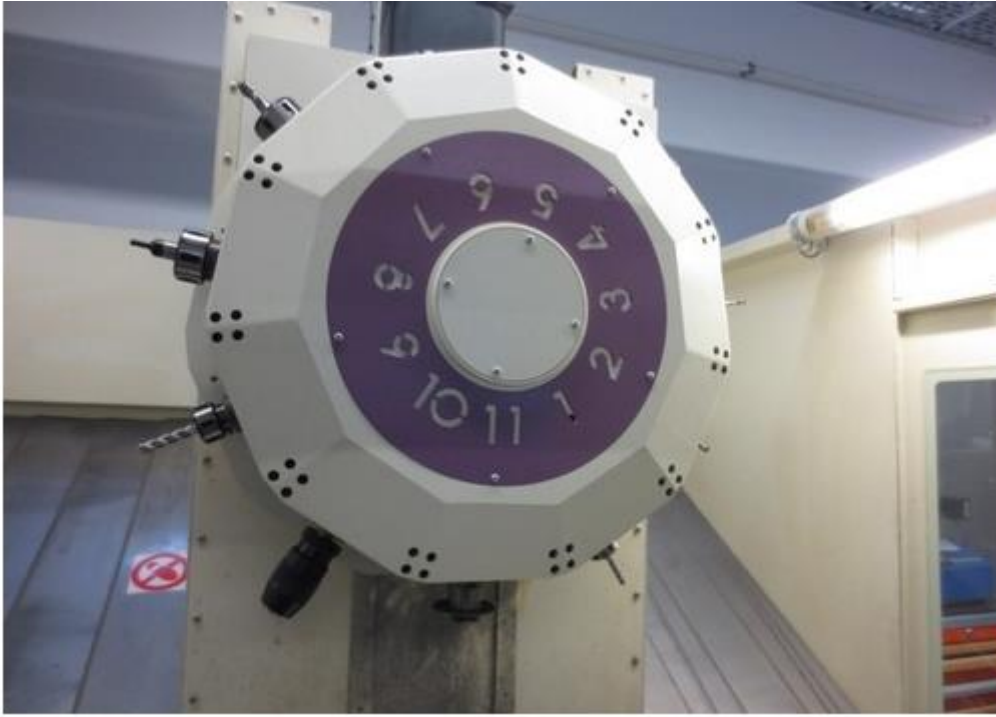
Магазин револьверного типа у обрабатывающего центра
